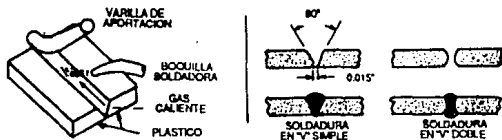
Soldadura con gas. (Ref. 2).
